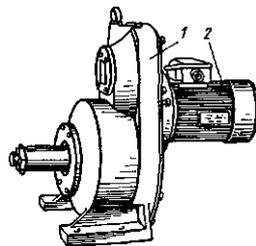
Мотор-редуктор: 1 – редуктор, 2- электродвигатель
